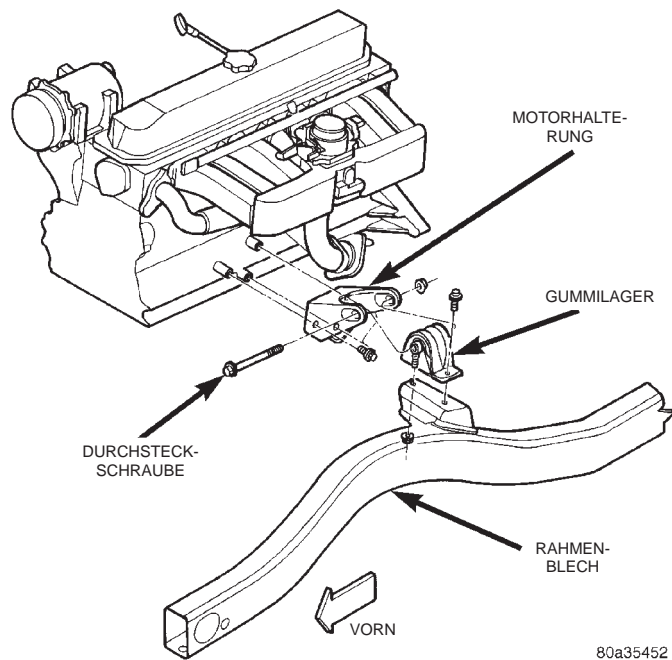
Motoraufhängung vorne links—4.0L-Motor
